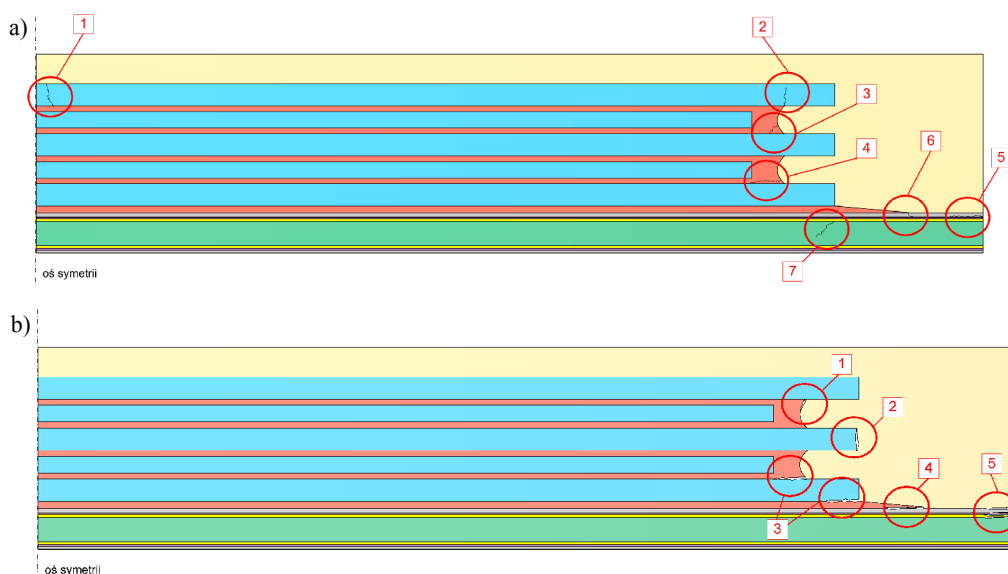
Przykłady montażu typu 3D, w przypadku struktur (a) i układów (b)
